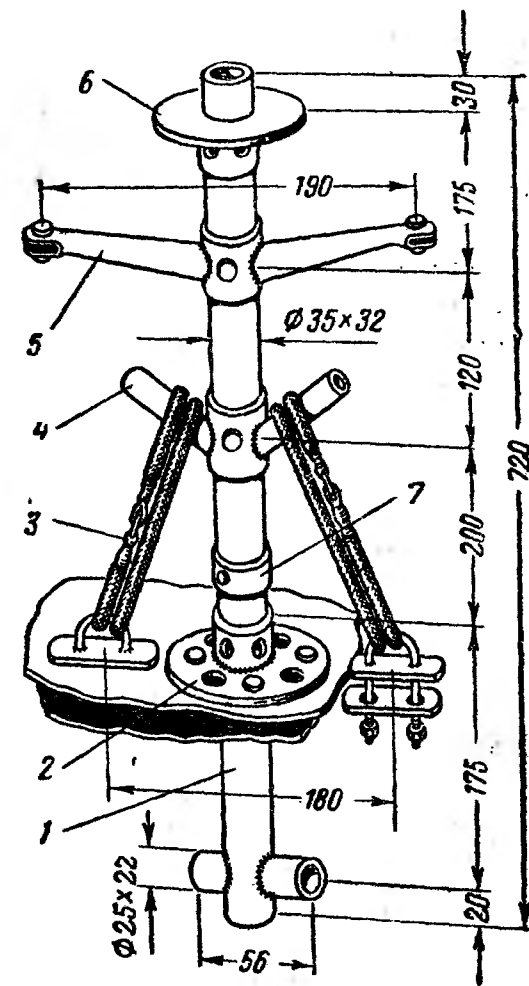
Колонка передней подвески аэросаней «ОСГА-4»: 1 — осевая труба; 2 — нижний фланец; 3 — резиновый амортизационный шнур; 4 — вилка; 5 — румпель; 6 — верхний фланец; 7 — упорное кольцо.
